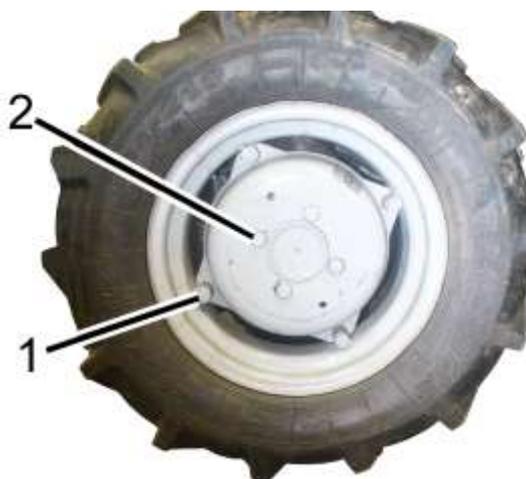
Проверка затяжки резьбовых соединений крепления колес
